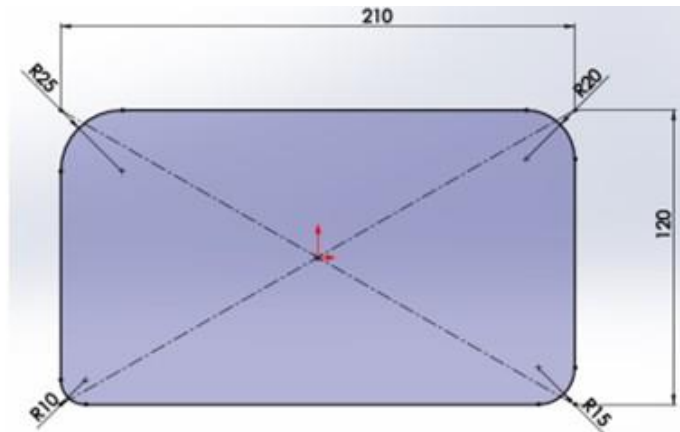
Dimensões em milímetros da primeira placa do molde.
